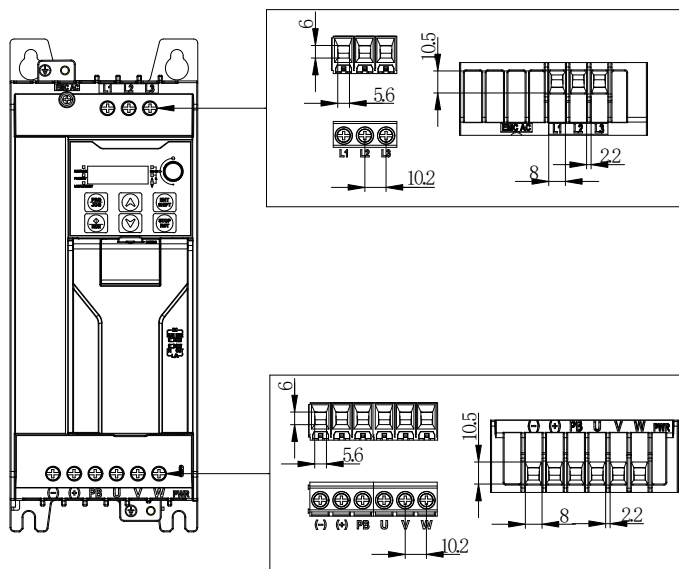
Клеммы главной цепи (Типоразмер типа D)
